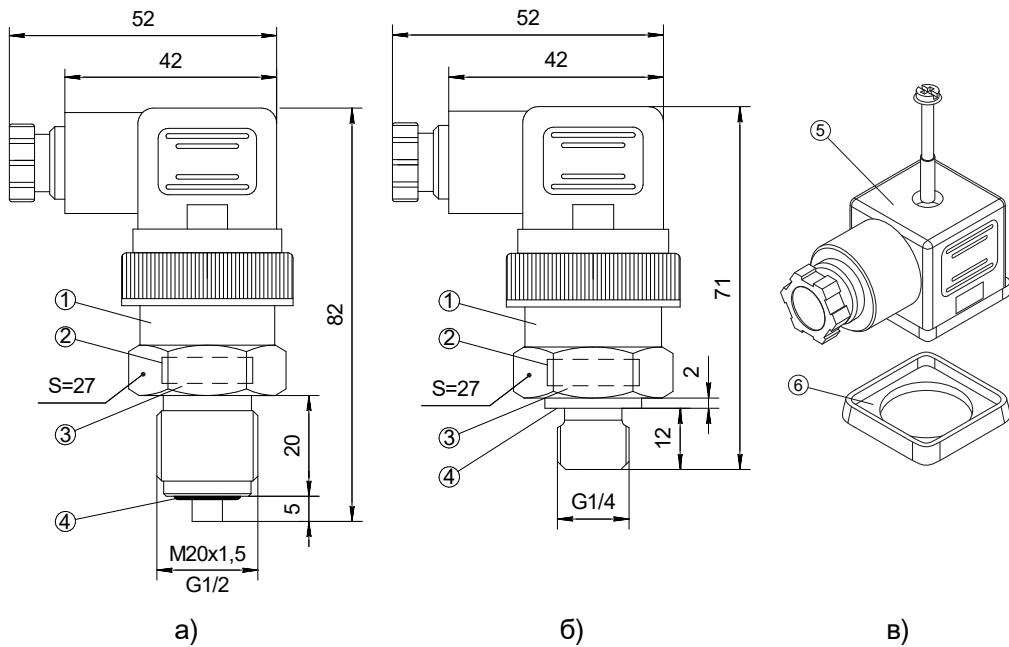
Габаритные размеры и состав конструкции датчика:
